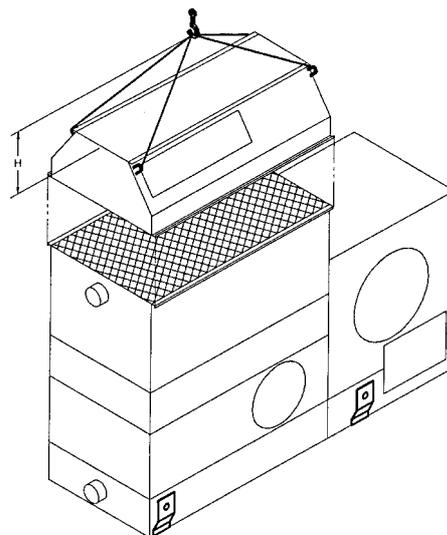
Montage der Ausblashaube (konische Ausführung)
